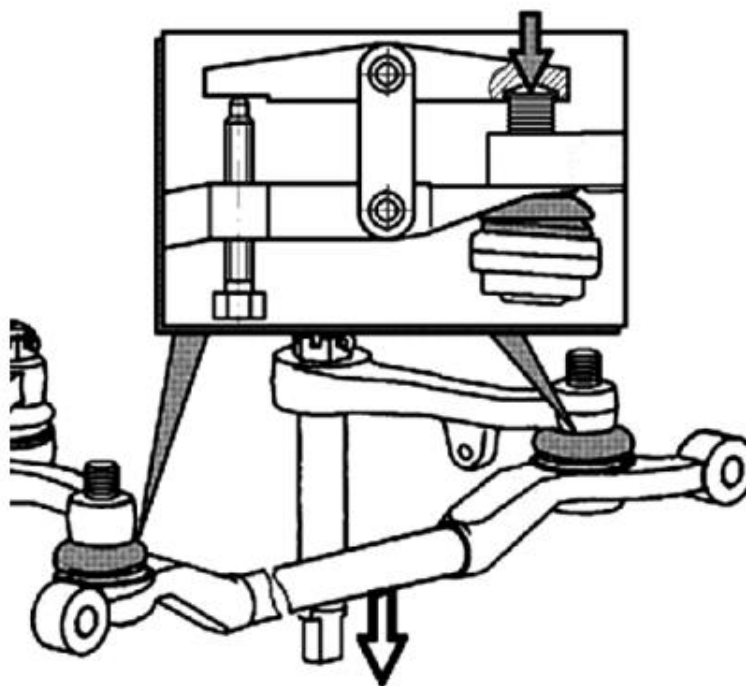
Внешний вид универсального съемника для выпрессовки шаровых пальцев
